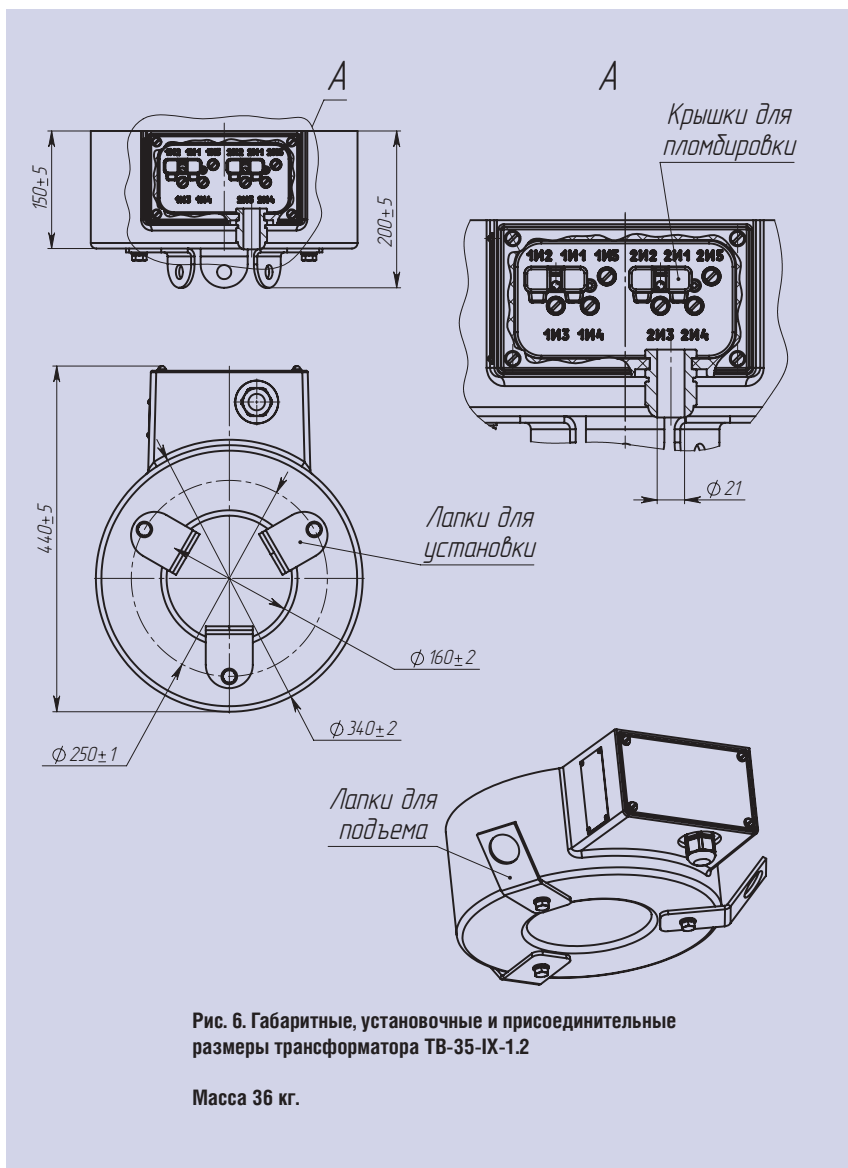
Габаритные, установочные и присоединительные размеры трансформатора ТВ-35-IX-1.2
